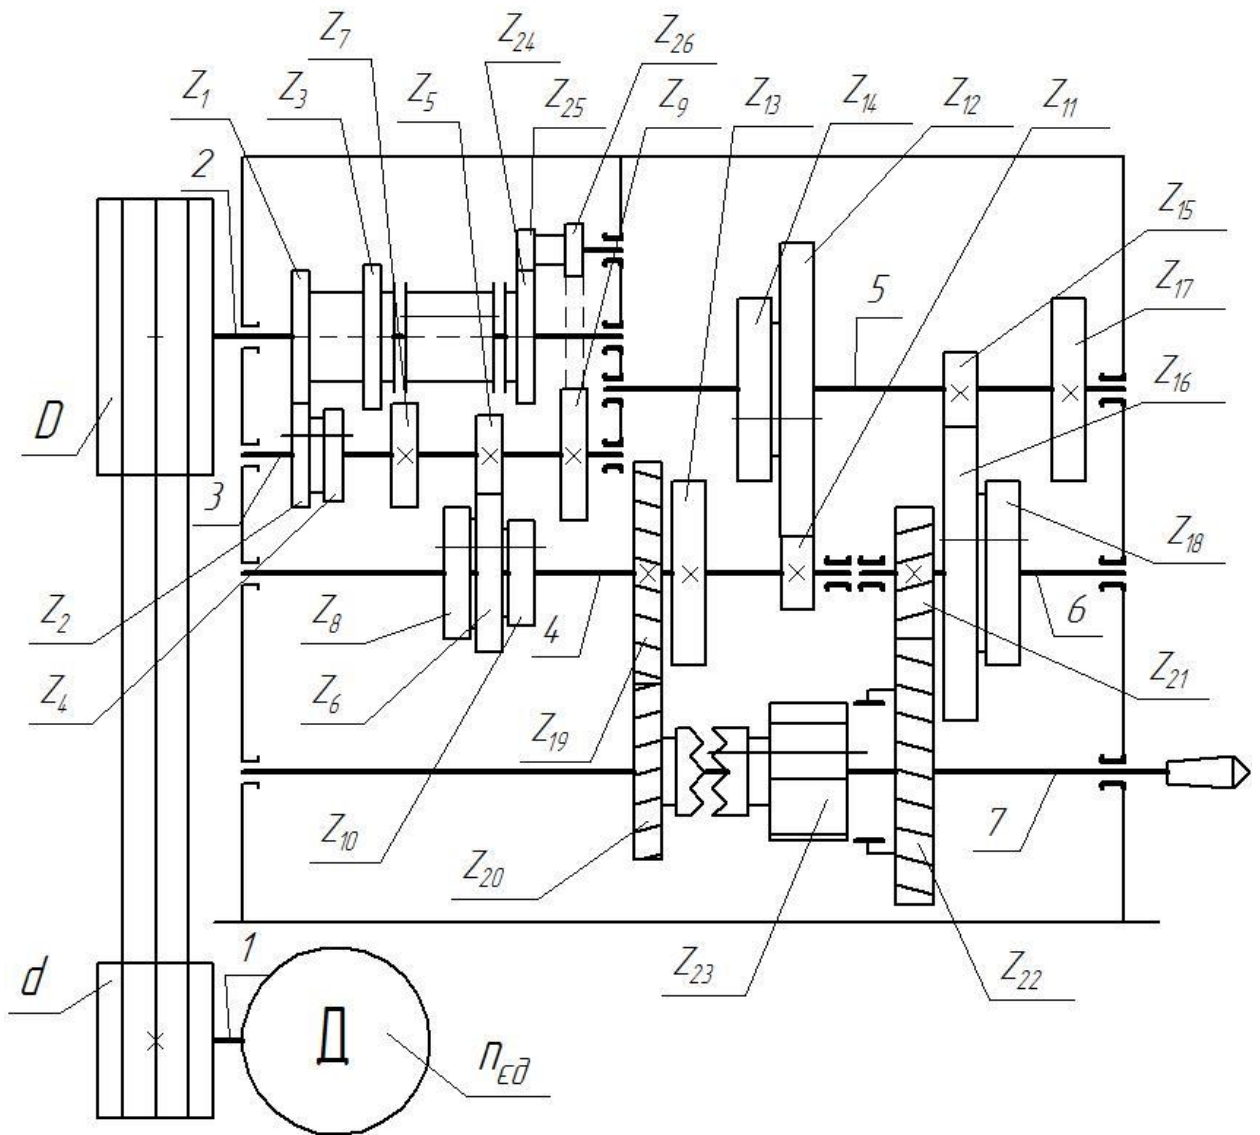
Кінематична схема привода головного руху верстату 1А62
